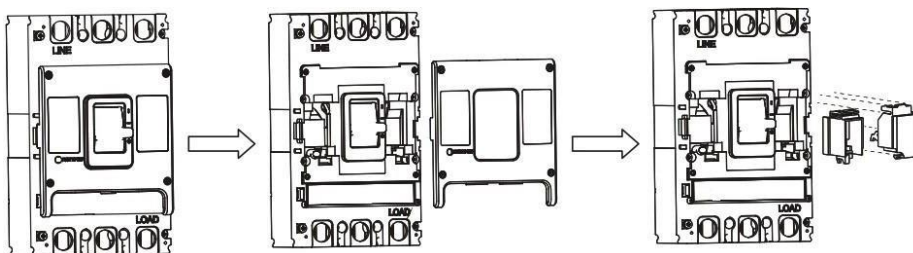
Схема установки аксессуаров внутрь корпуса аппарата
